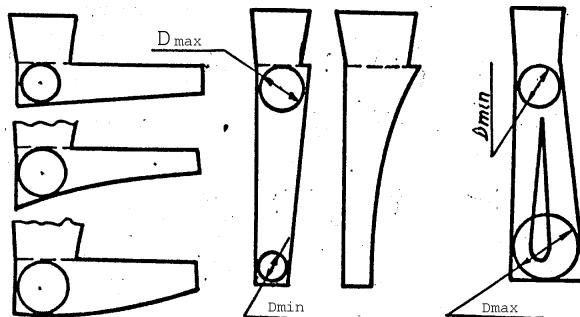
Отливки с плавно изменяющейся толщиной стенки.
